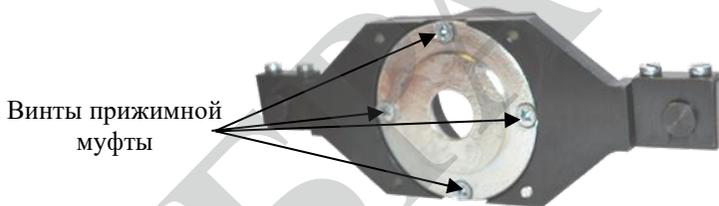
Смена прижимной муфты прибора Константа У2
